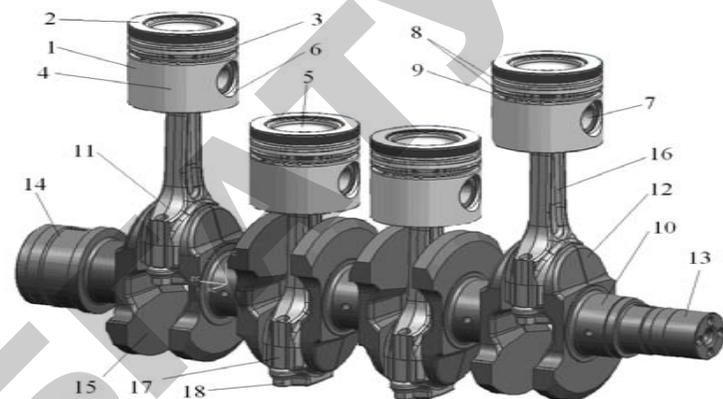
Кривошипно-шатунный механизм двигателя Д-245:
